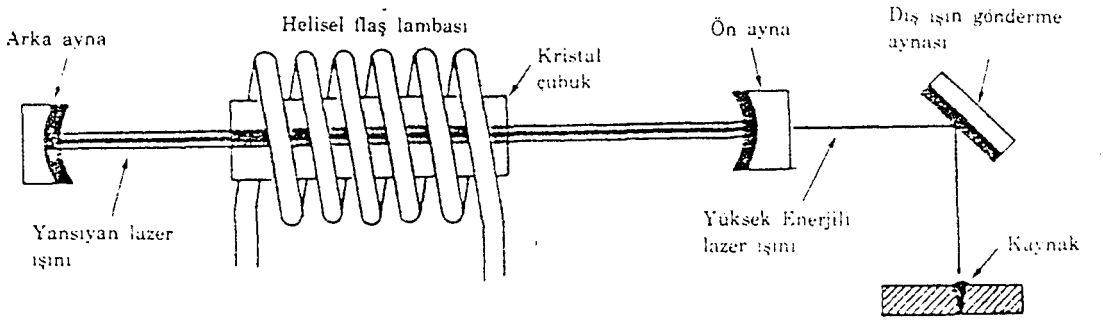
Ç1010 Malzemeye laser dikiş kaynağı
